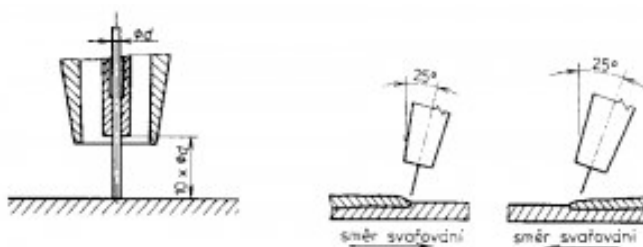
Svařování metodou 135 (MAG) [15]
